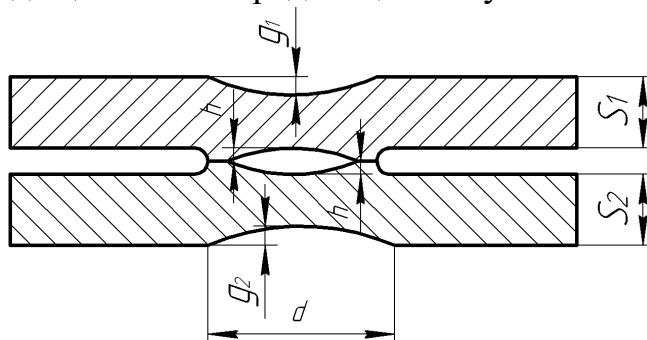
Конструктивные элементы соединений, выполненные контактной точечной сваркой
